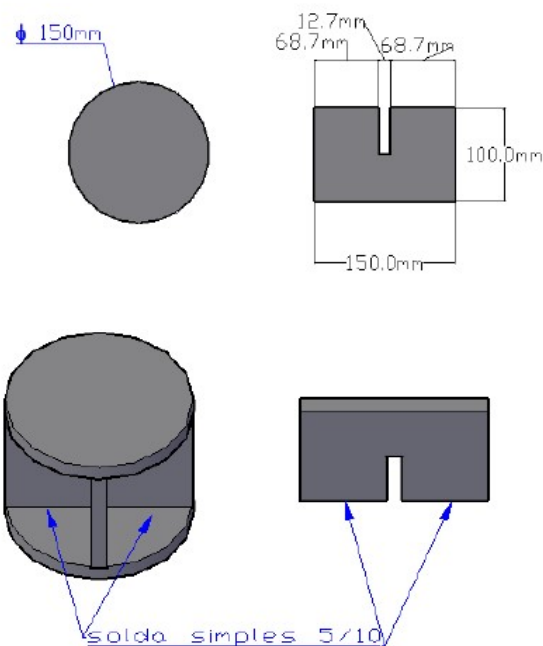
Projeto simplificado de suporte para ensaio de penetração. Fonte: Autor
